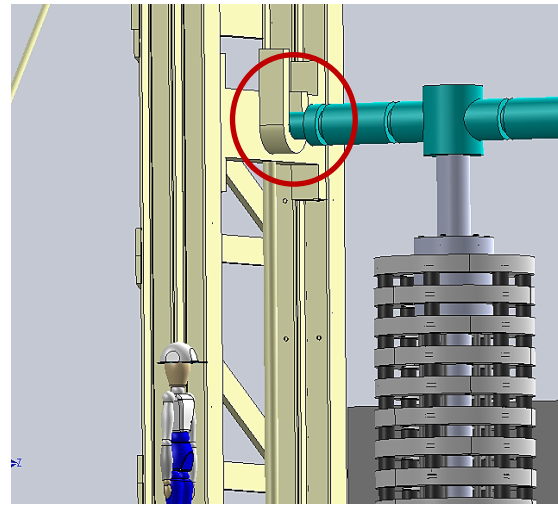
Vista de detalhe do rotor colocado no guiamento.
